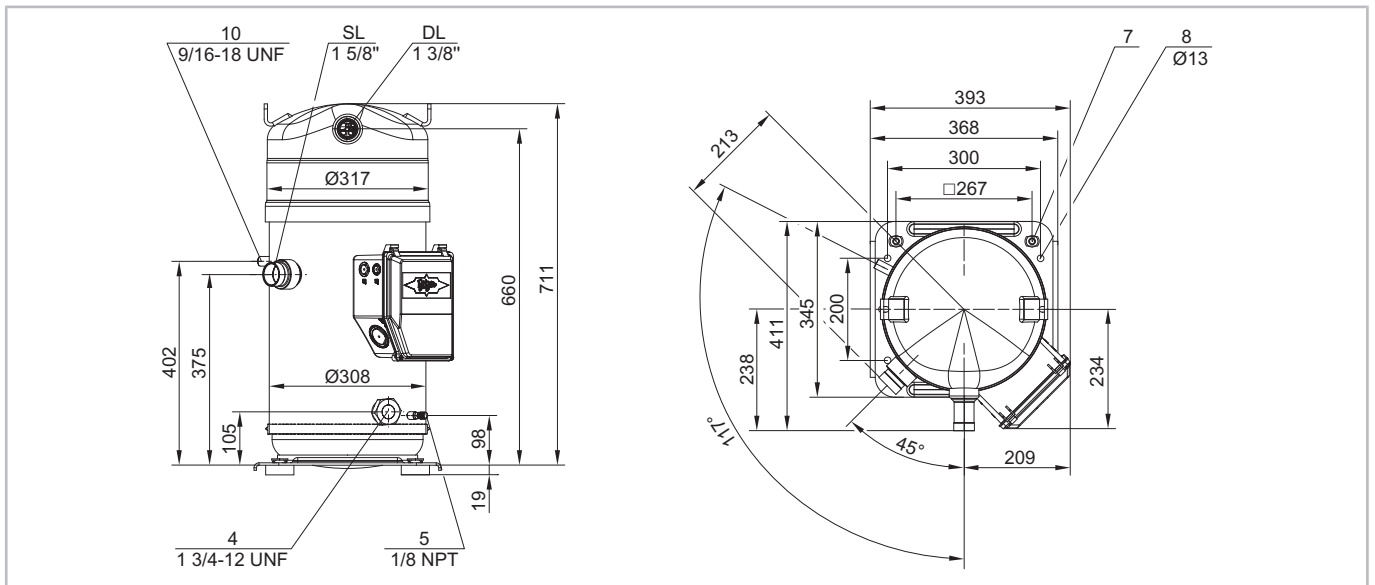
Maßzeichnungen ORBIT FIT: GED80295 .. GED80485
